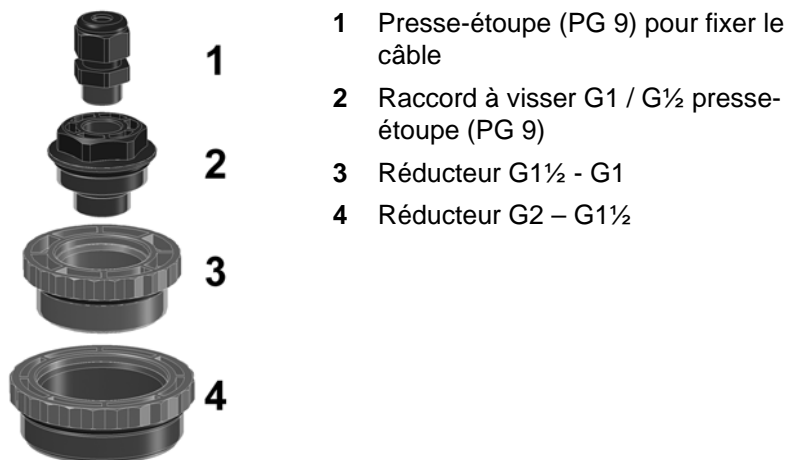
Montage sur le réservoir avec kit de presse-étoupe
